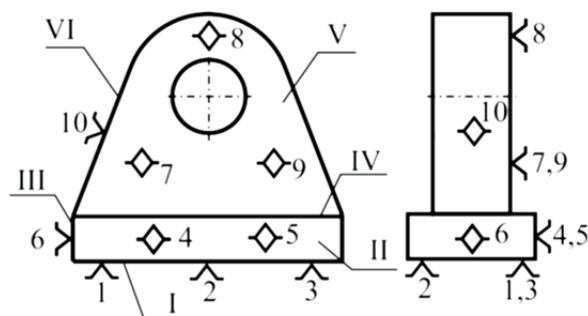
Схема базирования проушины при сборке из двух деталей
